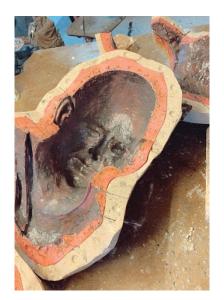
Proceso pincelado en molde de silicona con cera líquida.
